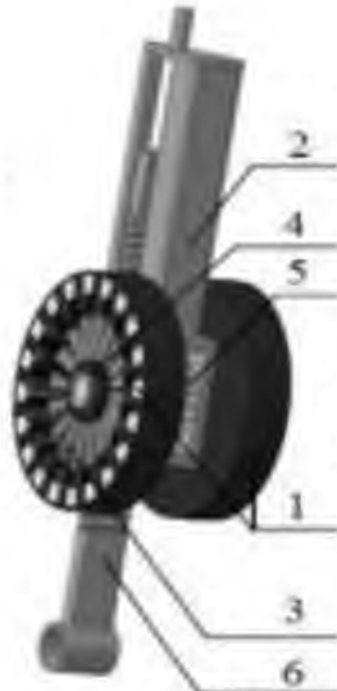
Конструкція регенеративного амортизатора з механізмом приводу, що складається з рейкової та конічної передачі
